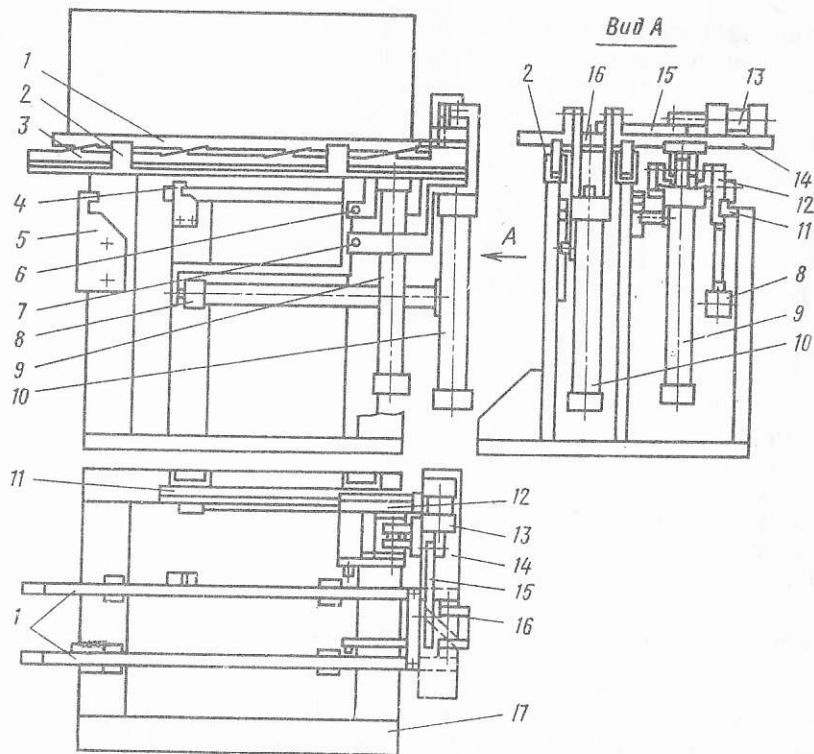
Устройство для загрузки заготовок на копировально-прошивочный станок
